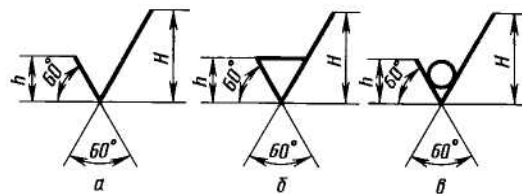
Знаки обозначения шероховатости на чертежах
